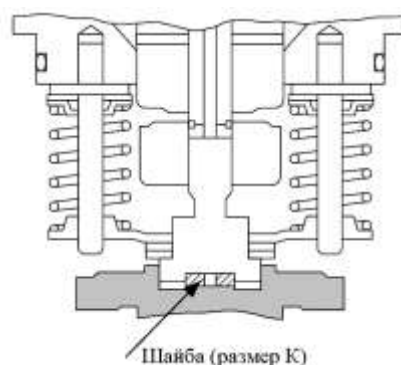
Схема плунжерной пары ТНВД типа VE в сборе с регулировочными шайбами и кулачковой шайбой.
